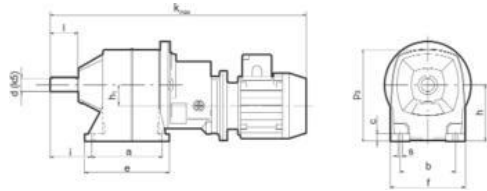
5МЛ3С–40...80ES на лапах, с цилиндрической приставкой
